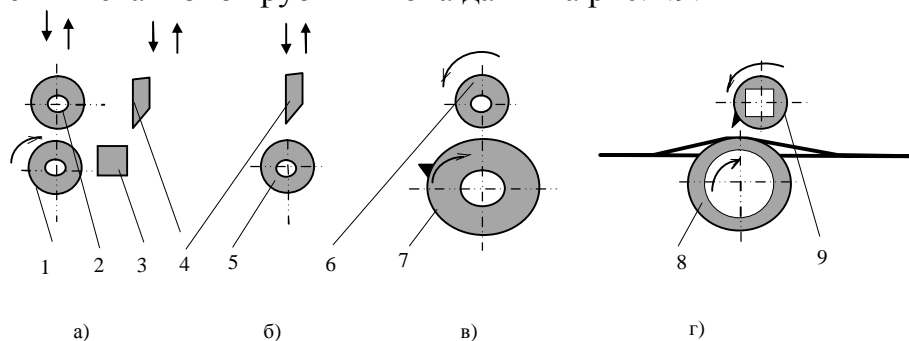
Схемы механизмов рубки шпона: а - с контрножом, б - с упругим элементом, в - с нижним ротором, г - с верхним ротором.(1 - ведущий подающий ролик, 2 - прижимной подающий ролик, 3 - контрнож, 4 - подвижный нож, 5 - эластичное основание, 6 - ножевой ротор, 7 - опорный барабан, 8 - обрезиненный барабан, 9 - ножевой ротор).
